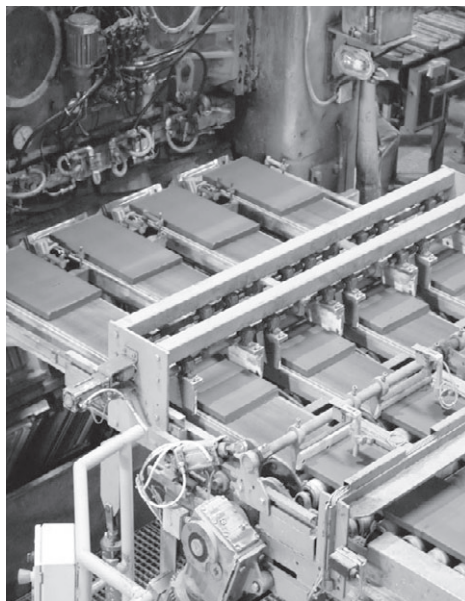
Процесс изготовления однообжиговой керамической плитки
